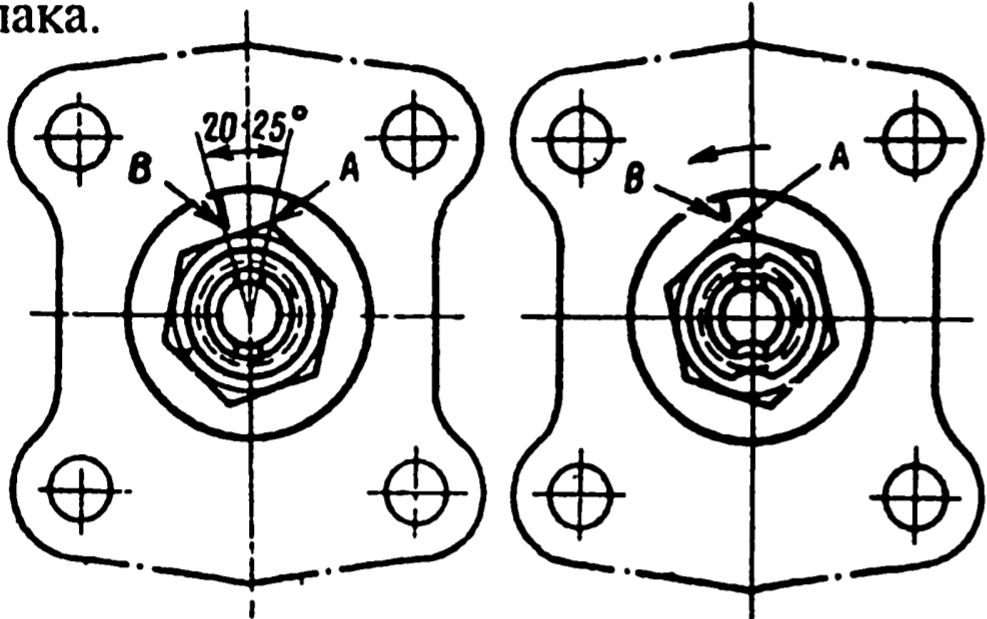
Схема регулировки подшипников ступиц передних колес: А - кромка гайки; В - метка на шайбе. Момент затягивания гайки 0,7 кгс·м. Ослабление гайки на 20-25°
